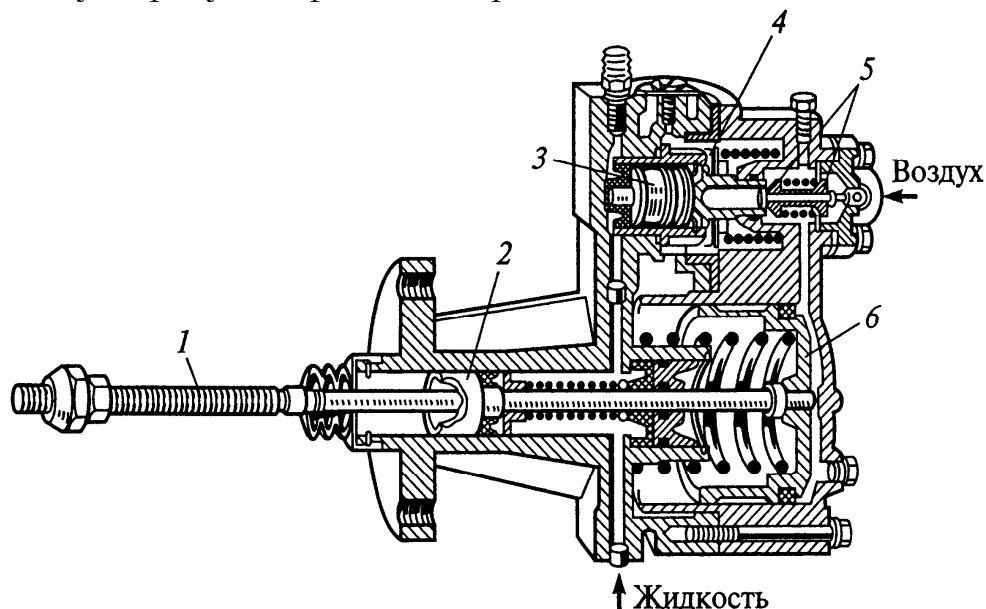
Пневмоусилитель привода сцепления грузовых автомобилей КамАЗ: 1 – шток; 2, 3, 6 – поршни; 4 – диафрагма; 5 – клапаны
